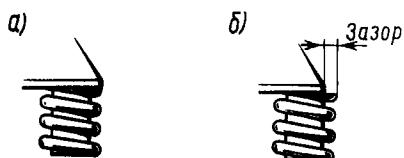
Взаимное положение наружных пружин рессорного комплекта и надрессорной балки:
